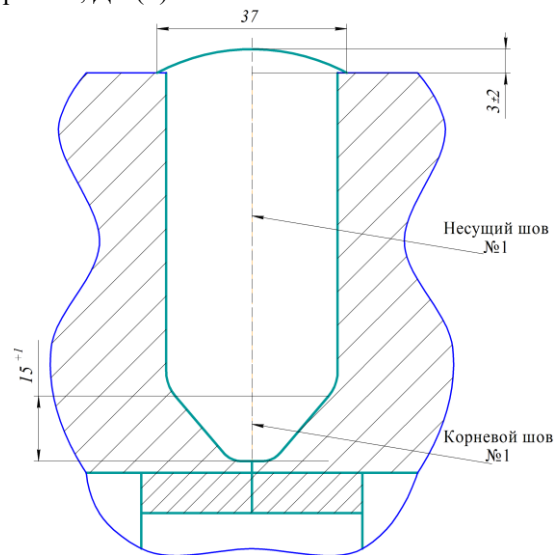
Схема сварного соединения опытного образца из стали 25X2НМФА
